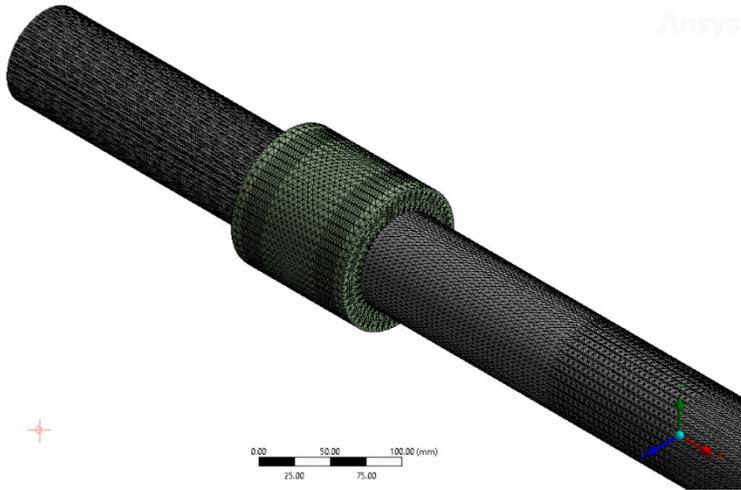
Modelado y discretizado de la columna guía para en detalle.
